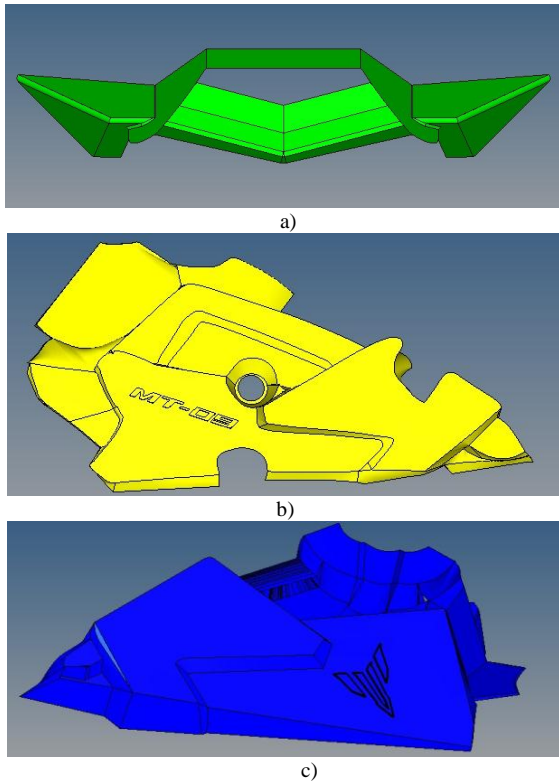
Piezas para el proceso a) Pieza Frontal, b) Pieza Derecha, c) Parte Izquierda.
